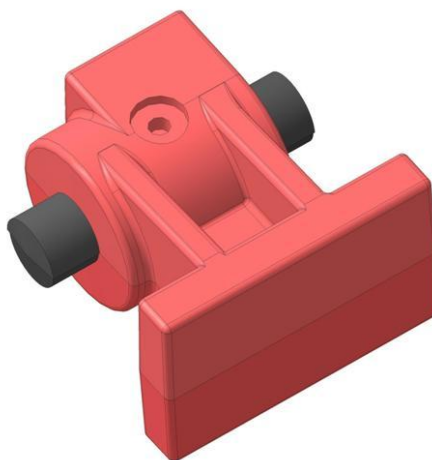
Общий вид модели отливки детали «Кронштейн» в сборе
